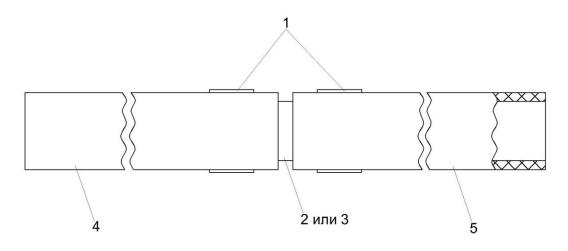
Рукав сборный КЗК-12-0601600-01
